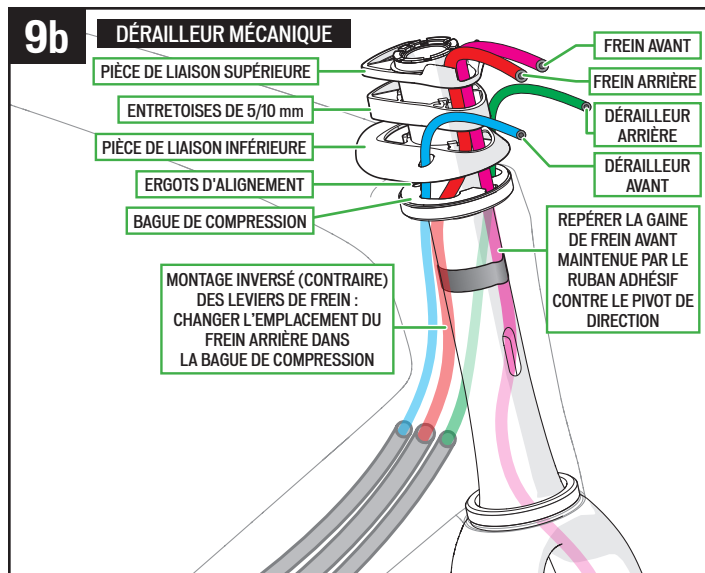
installation des pièces de liaison et du stack (dérailleur mécanique).
